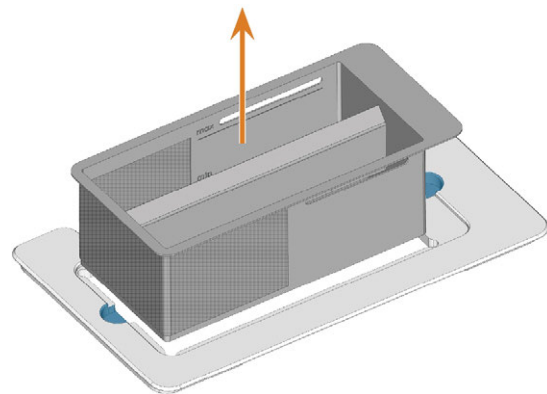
RETIRER LE PANIER-FILTRE (SURFACES RENFORCÉES MARQUÉES EN BLEU)
